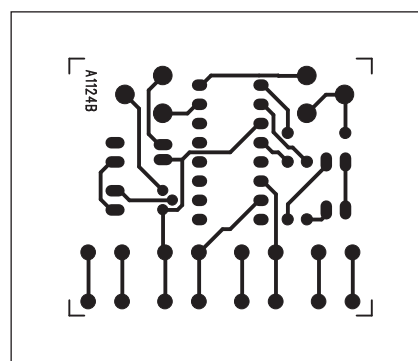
Obrazec desky spojů generátoru zvukových efektů (strana TOP)
